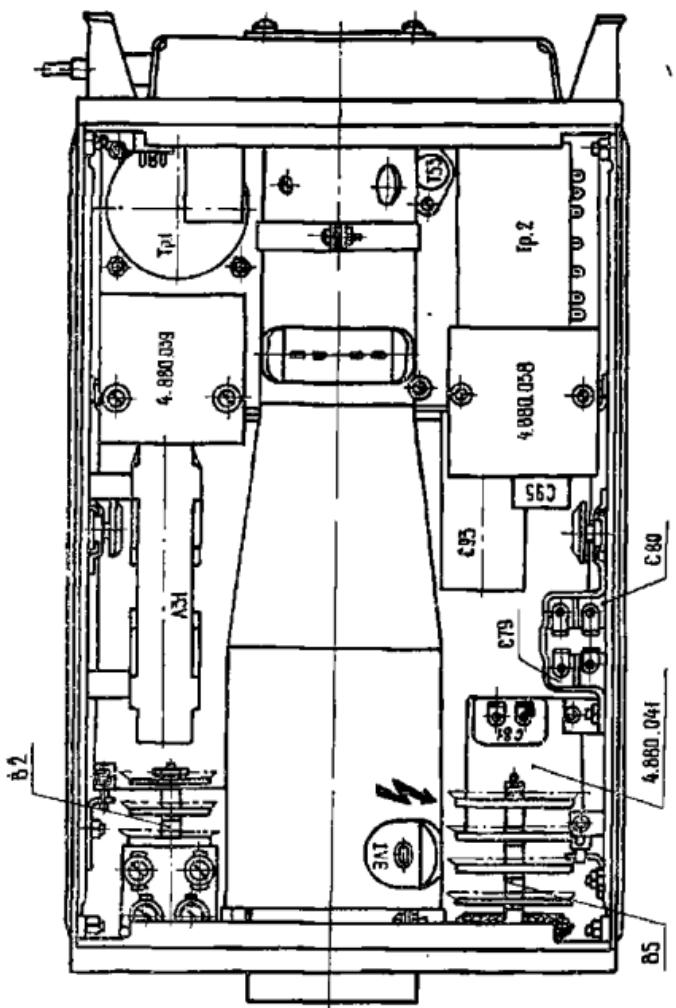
Схема расположения установленных элементов и печатных плат (вид сверху)
